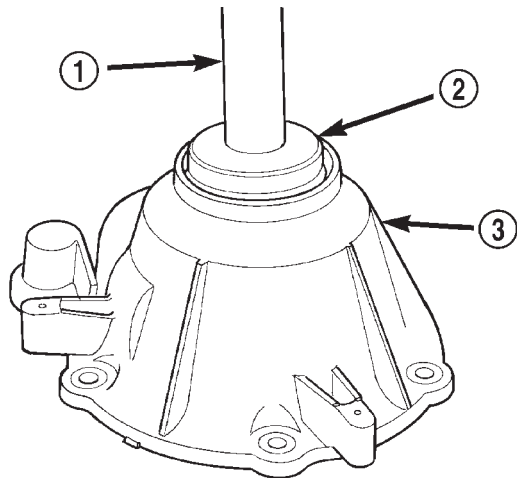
Instalación del cojinete trasero del eje transmisor delantero
